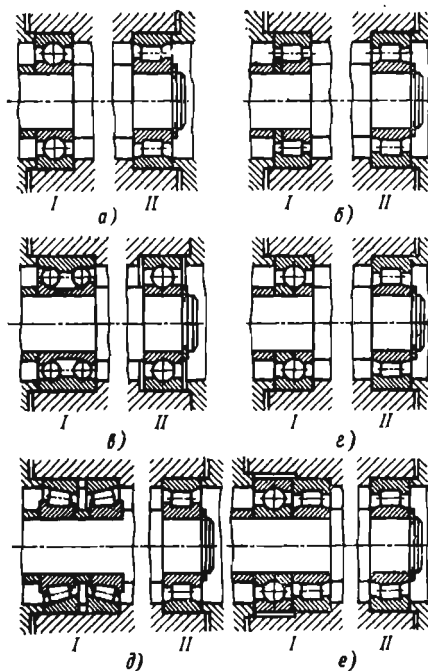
Схемы установки подшипников в «фиксирующей — плавающей» опорах: I — фиксирующая опора; II — плавающая опора
